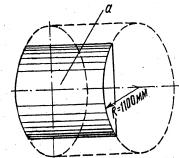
Схема наладки станка для обработки торцов деталей по криволинейному контуру.
